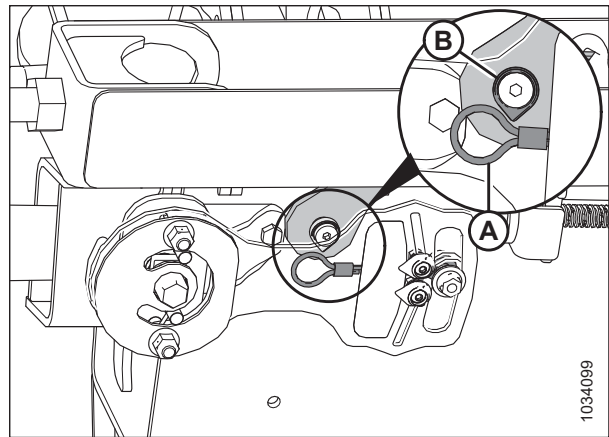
Serrure à câble FlexChecker - Côté gauche
